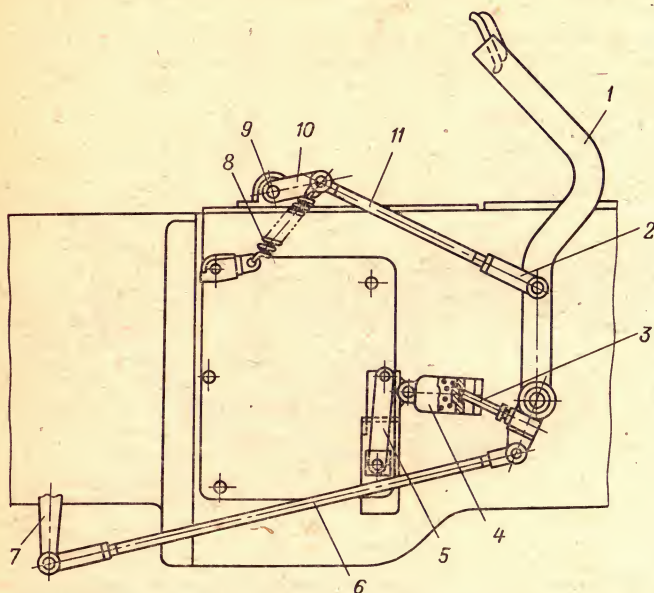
Управление муфтой сцепления тракторов ЮМЗ-6М и ЮМЗ-6Л: 1 — педаль; 2 — вилка; 3 — упорный винт; 4 — сервоусилитель; 5 — кронштейн; 6 — тяга; 7 — рычаг выключения сцепления; 8 — пружина; 9 — валик блокировочный; 10 — рычаг валика блокировочного; 11 — тяга блокировочного механизма
